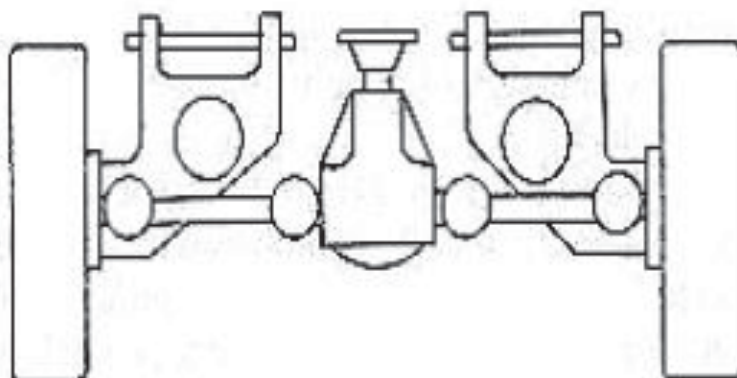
Esquematico de suspensão do tipo braço arrastado aplicado em suspensões traseiras. (Barbieri 2008).
